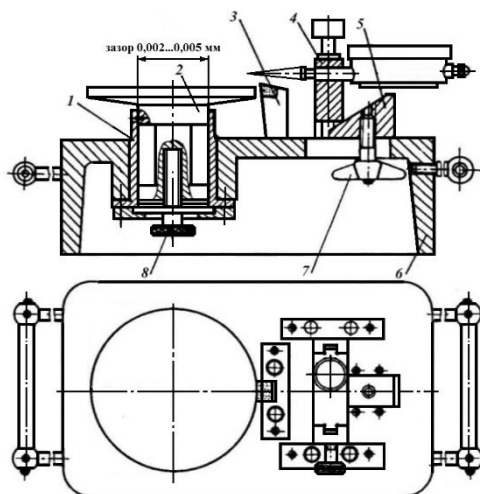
Приспособление для контроля неперпендикулярности образующей деталей типа «шайба»
